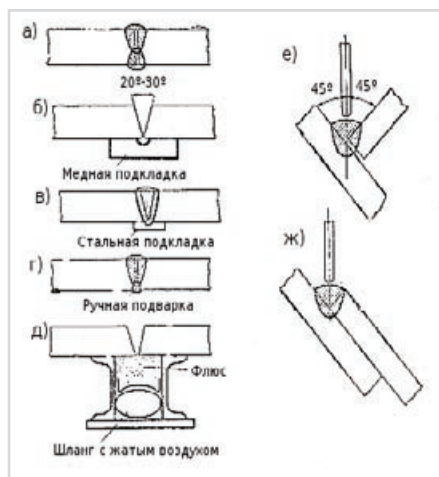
Способы автоматической сварки стыковых швов
